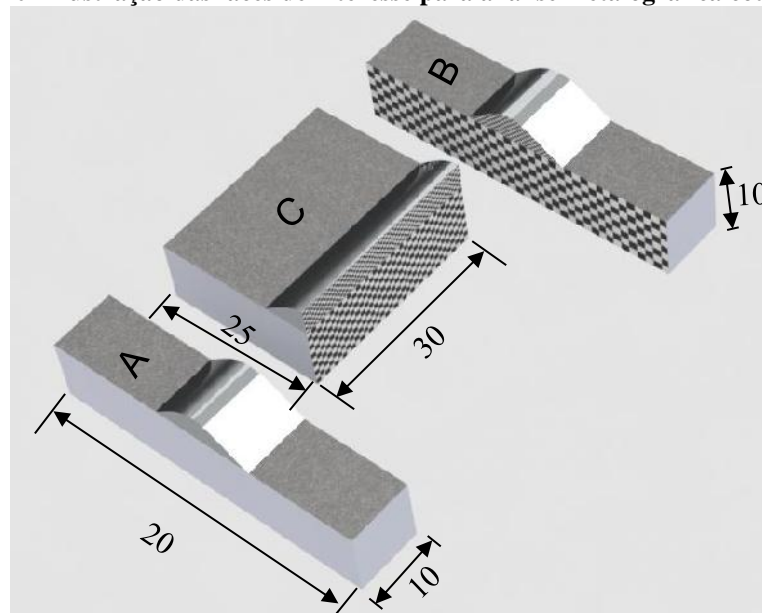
Esquema de retirada das amostras soldadas para o preparo metalográfico. Cotas em (mm)
